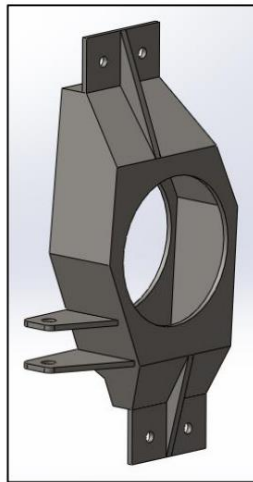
Proceso de diseño CAD de la mangueta delantera.
